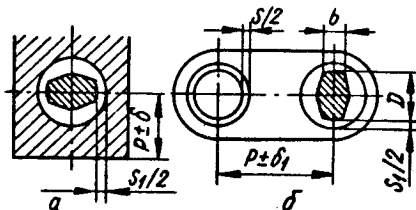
Приклади для розрахунку ширини циліндричної частини зрізаного пальця:
